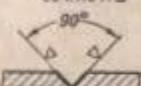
Подготовка трещин в кожухе под сварку
